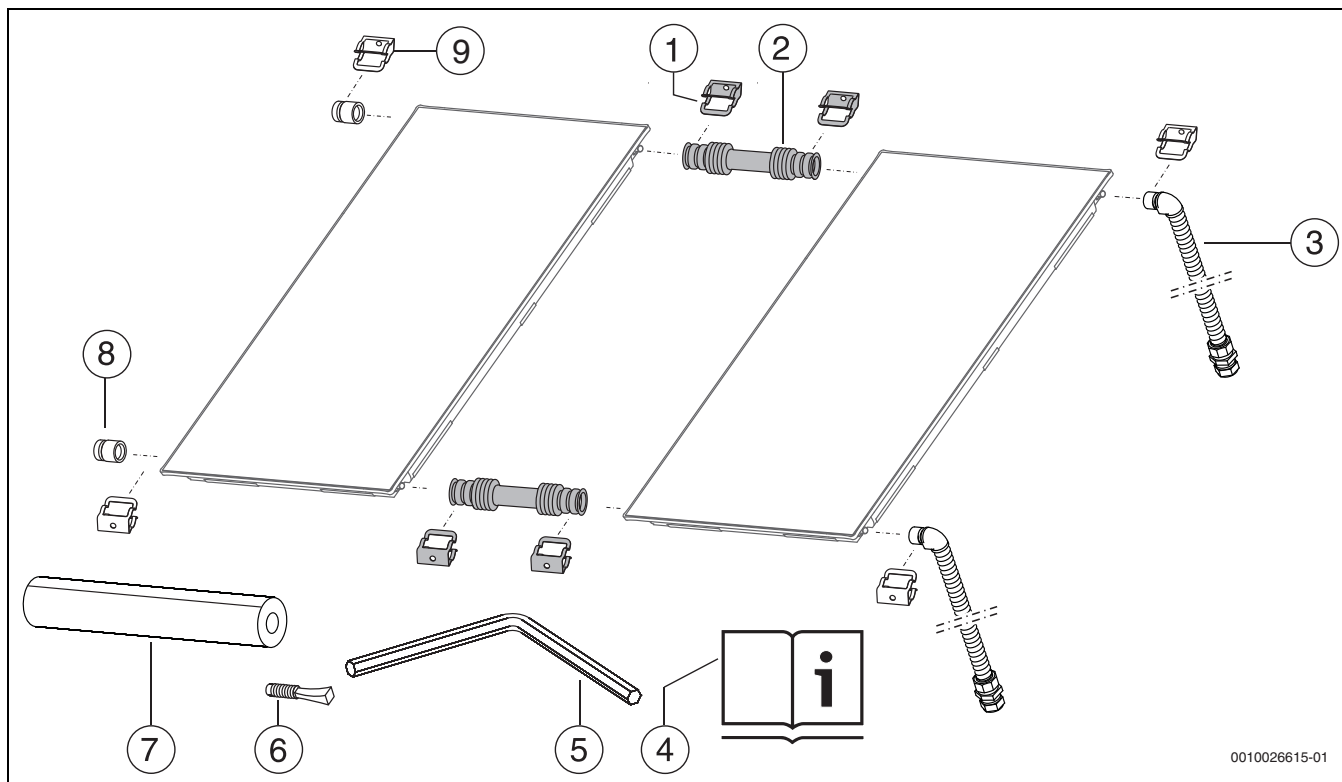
1 set raccordi di collegamento sul tetto e 2 set di collegamento (grigi)
